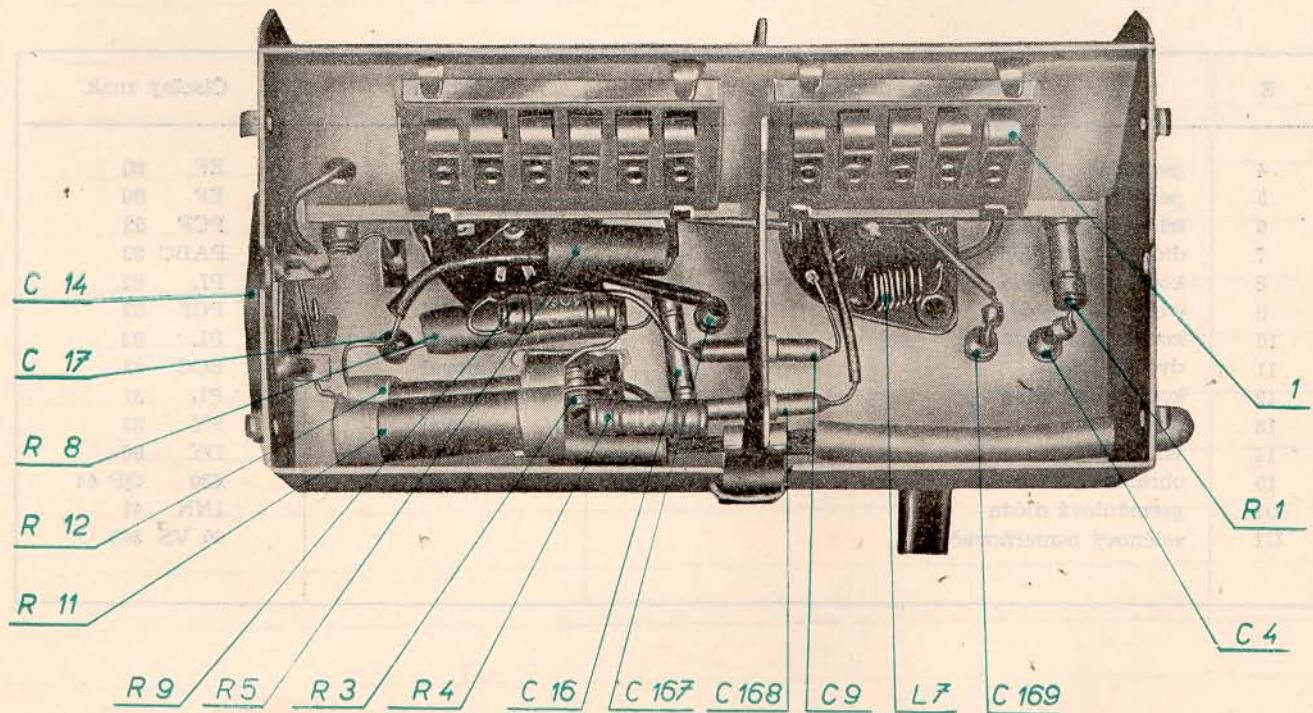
Rozmiestnenie dôležitých dielov pod chassis
